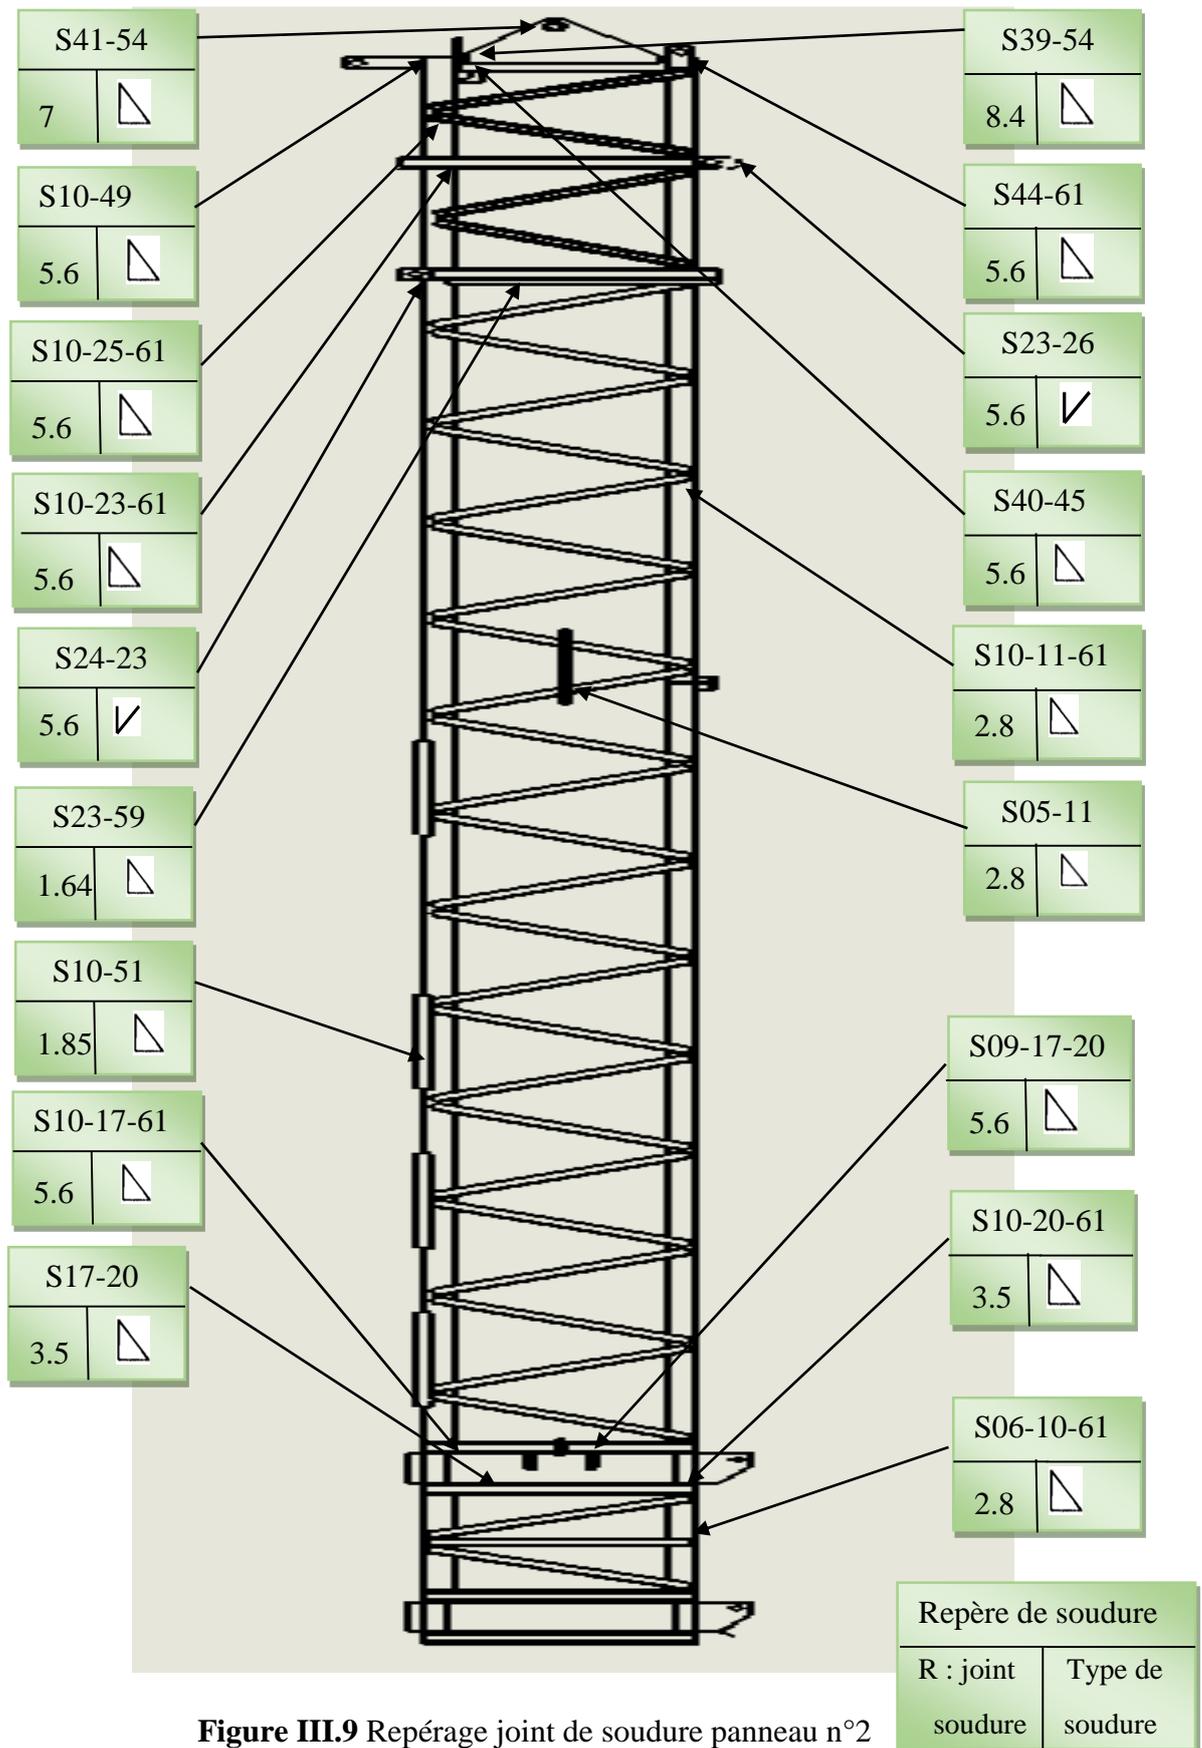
Repérage joint de soudure panneau n°2
